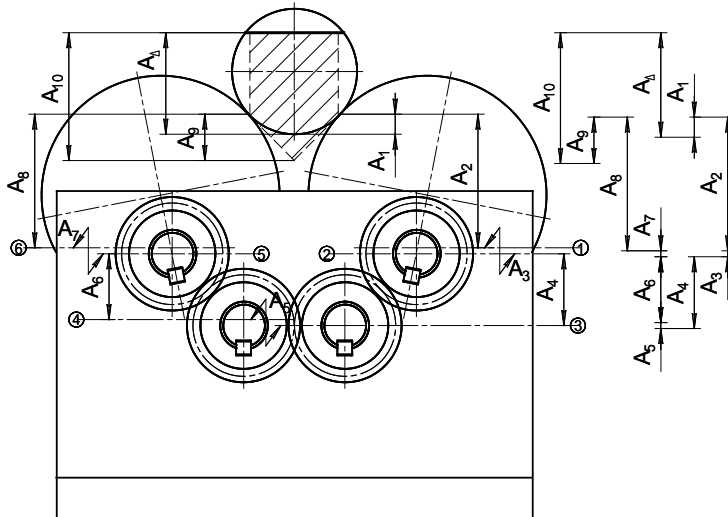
Базуюча призма і розмірний ланцюг для визначення похибки базування вала при фрезеруванні лиски, паралельної робочому столу верстата
